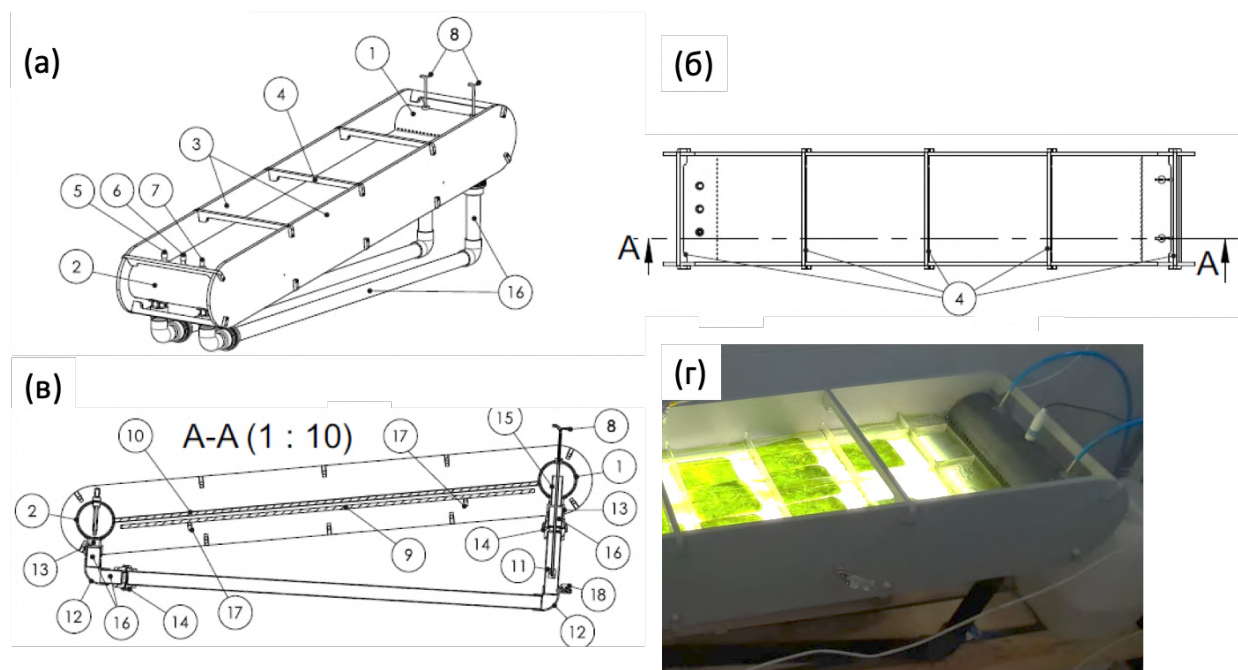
Тонкослойный каскад: сборочный чертёж — общий вид (а), вид сверху (б), вид сбоку (в), а также изображение работающей установки с АБС (г). Обозначения: 1 — резервуар верхний, 2 — резервуар нижний, 3 — боковая пластина, 4 — ребро жёсткости, 5 — датчик температуры, 6 — датчик рН, 7 — датчик O₂, 8 — инжектор, 9 — световая панель, 10 — панель светопрозрачная, 11 — распылитель, 12 — уголок, 13 — седёлка, 14 — муфта, 15 — горловина эрлифта, 16 — сегмент обводной трубы, 17 — упор световой панели, 18 — сливной кран.
